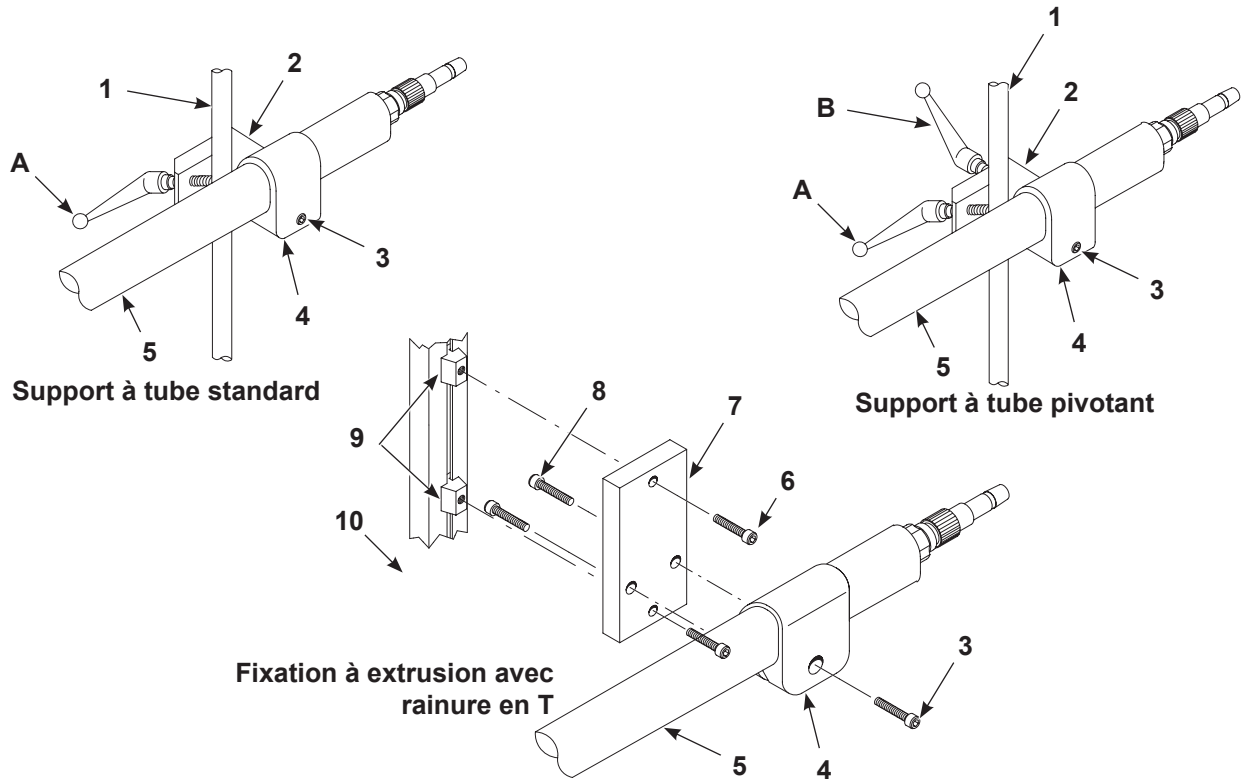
Éléments de fixation pour pistolet à fixation sur tube
